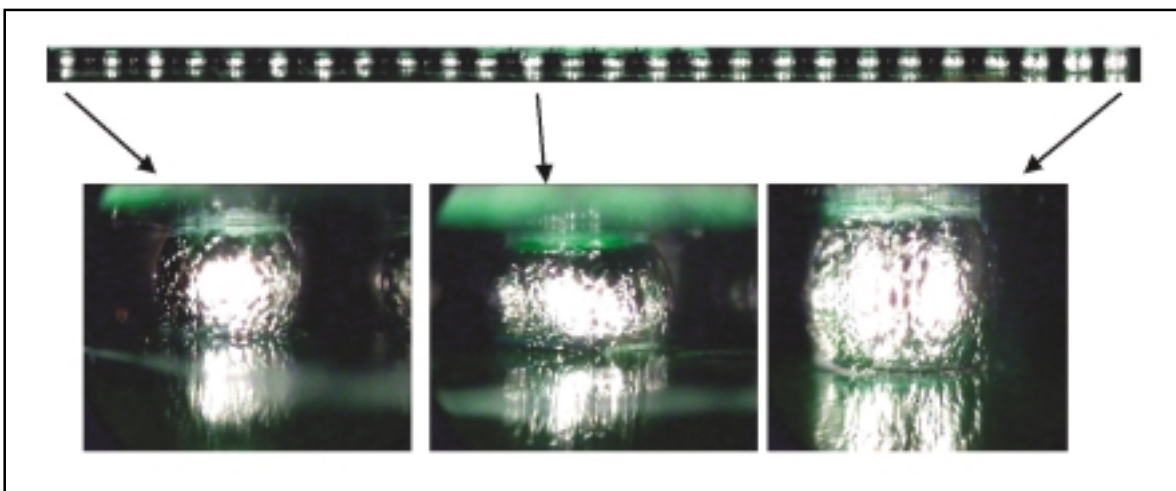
Bolas a lo largo del borde del BGA afectadas por el cambio de forma del encapsulado y de la placa.
